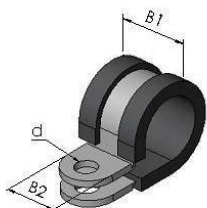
gedrehte Ausführung für den Einsatz mit Klemmringen
